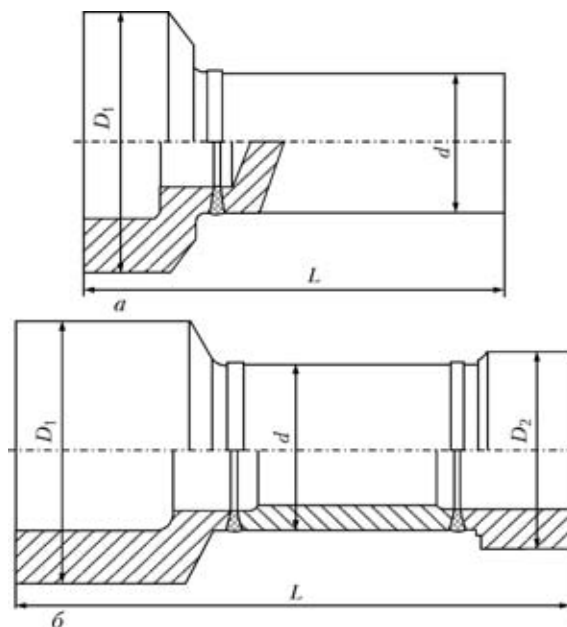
Схемы сварных заготовок шлицевого (а) и шарнирного (б) валов
